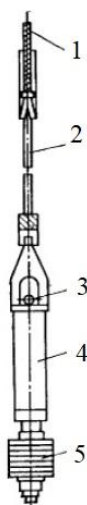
Устройство сваба: 1 – канат, 2 – подвеска, 3 – клапан, 4 – патрубок, 5 – поршень
